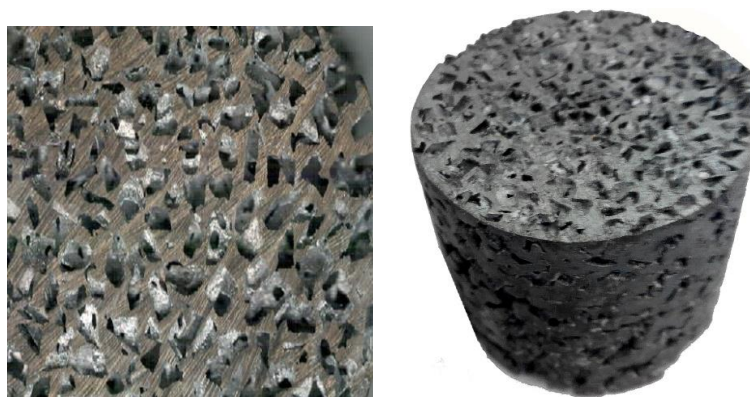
Пористая заготовка - преформа из матричного алюминиевого сплава для ввода в поры частиц малого размера, в том числе и наноразмерных
